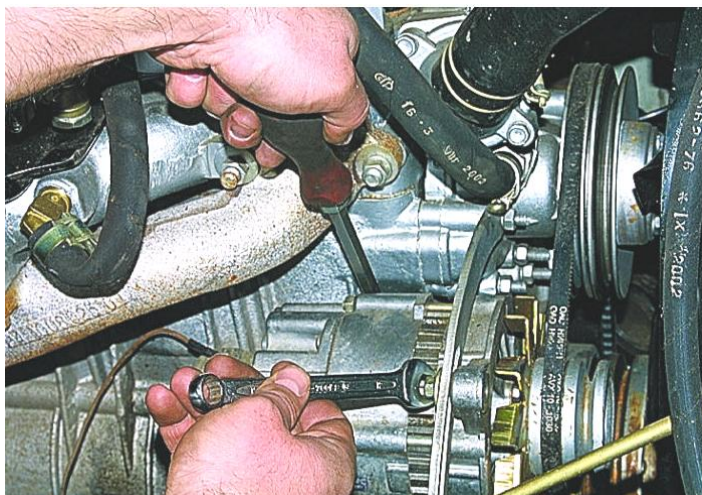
Натяг пасу приводу вентилятора шляхом переміщення корпусу генератора з шківом
